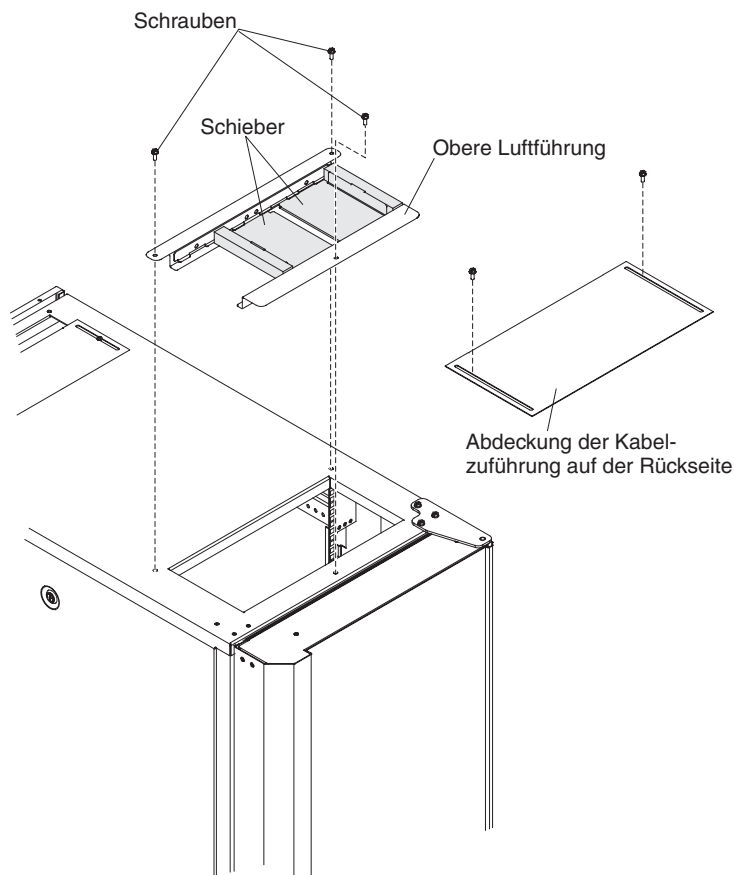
Hintere Abdeckung für die Kabelzuführung abnehmen und obere Luftführung installieren
